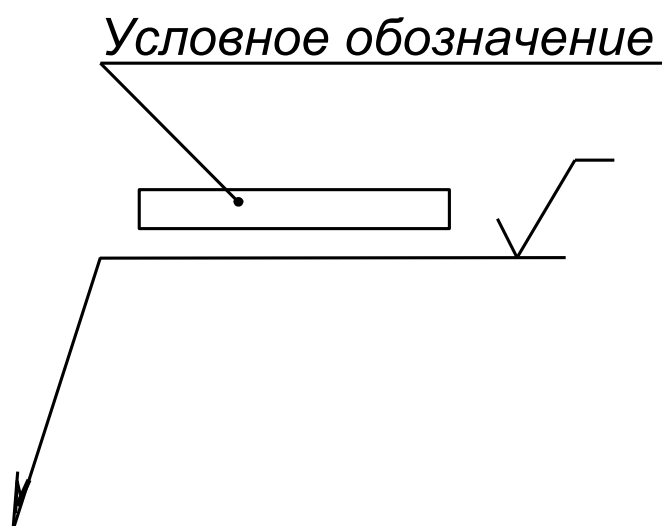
Обозначение шероховатости механически обработанной поверхности шва
